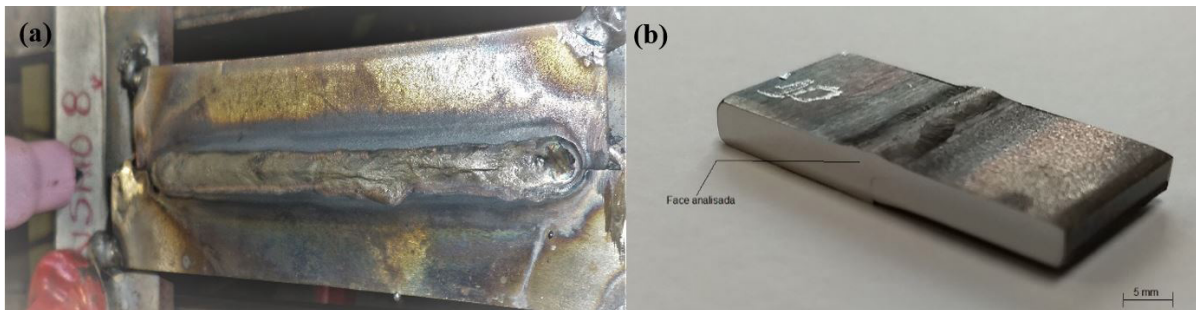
(a) Corpo de Prova após processo de soldagem multipasse; e (b) corpo de prova cortado para realização de análise de sua seção transversal.
